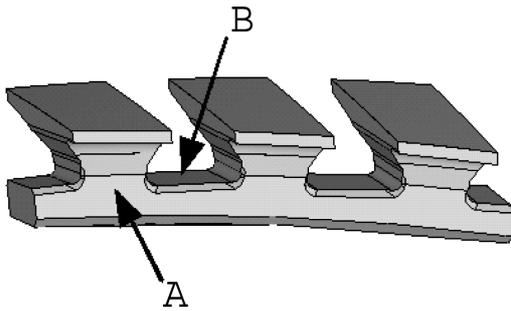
Фрагмент ободной части диска компрессора высокого давления с пазами типа "ласточкин хвост": А – боковая поверхность ножки межпазового выступа, В – доньшко паза.
